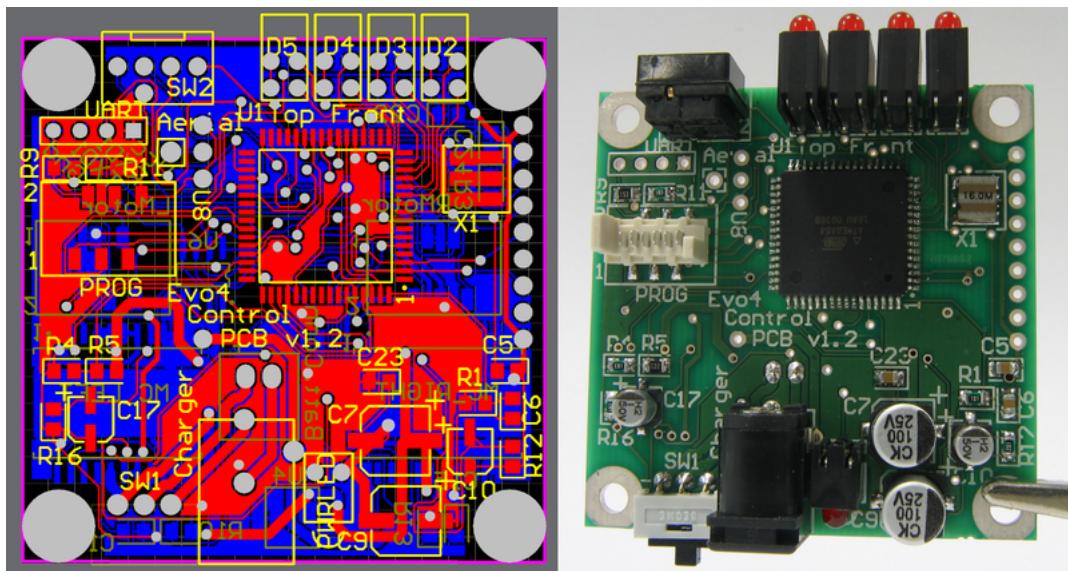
Vom Layout zur Printplatte (PCB Design, 2007)
